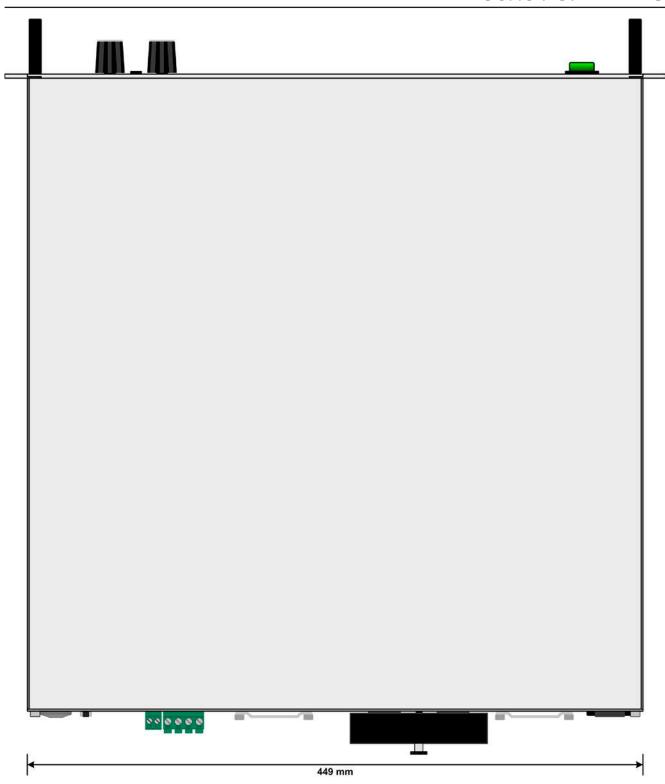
Vista desde arriba, con cubierta DC (terminal tipo 1)
